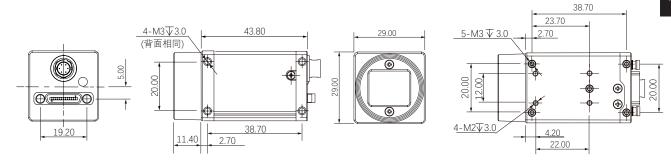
29 * 29 * 43.8mm 相机的物理尺寸(含 6Pin I/O 接口)。
